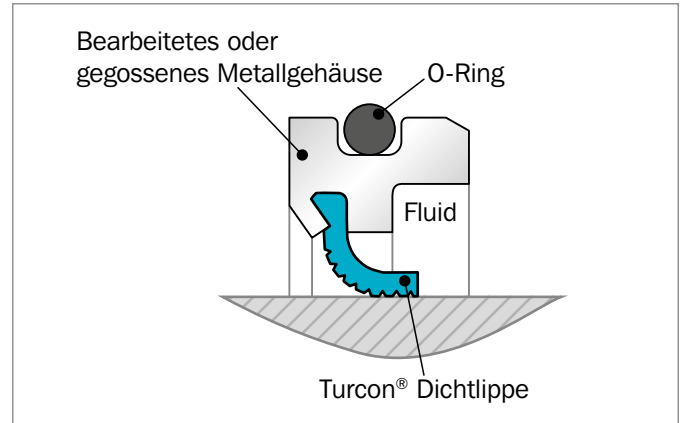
O-Ring-Ausführung; Für Passungen mit geringer Überdeckung im Gehäuse; Oberflächengüte des Einbauraums > 0,8 µm Ra
